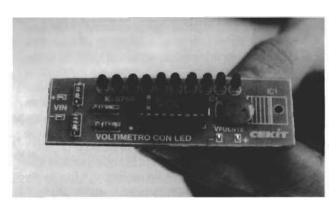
El ensamble de la tarieta es muy sencillo. Se debe poner especial atención en el momento de hacer las soldaduras para no causar cortos entre puntos adyacentes. Además, en los sitios donde se conectan cables se deben poner espadines para facilitar la posterior soldadura de los mismos. Se recomienda que una vez se termine el proceso de soldadura, se haga una limpieza de la tarjeta con un poco de alcohol y un cepillo de dientes. Así se remueve la capa de material fundente que queda después de la soldadura. Note que el regulador de voltaje y los espadines, se colocan en al lado de la soldadura del circuito impreso, esto se hace con el fin de facilitar el montaje del voltímetro en la parte frontal de un chasís, tal como se ve en la figura 21.6.
